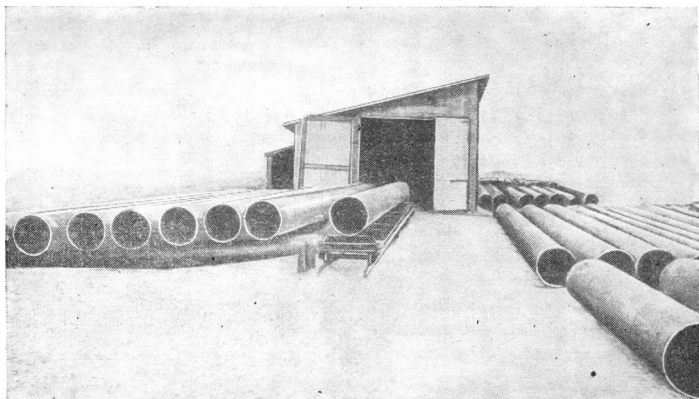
Базовые установки для сварки труб под слоем флюса
